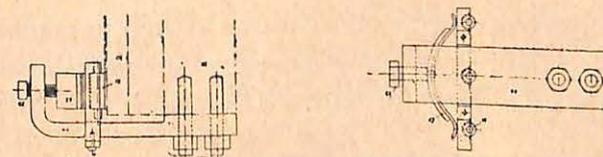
Four E. Coppée, dispositif de serrage du panneau de fermeture en profil et en plan.
